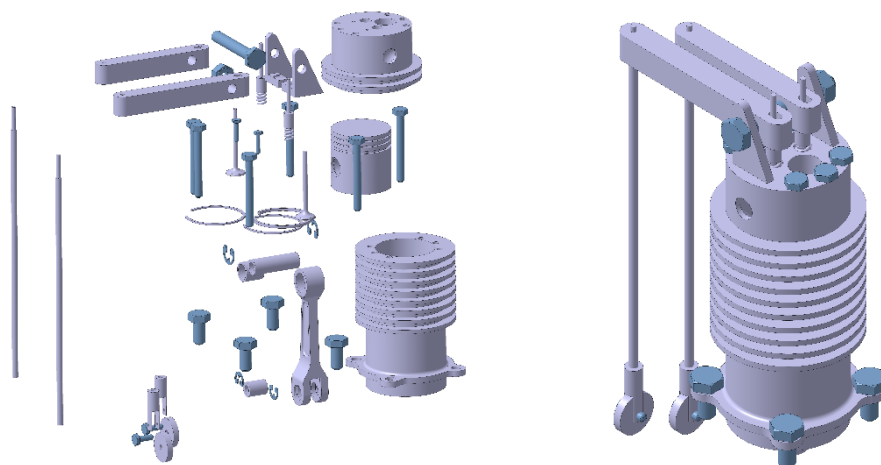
a la izquierda: vista explosionada del subconjunto cilindro-palancas. A la derecha: vista isométrica del subconjunto cilindro-palancas.
